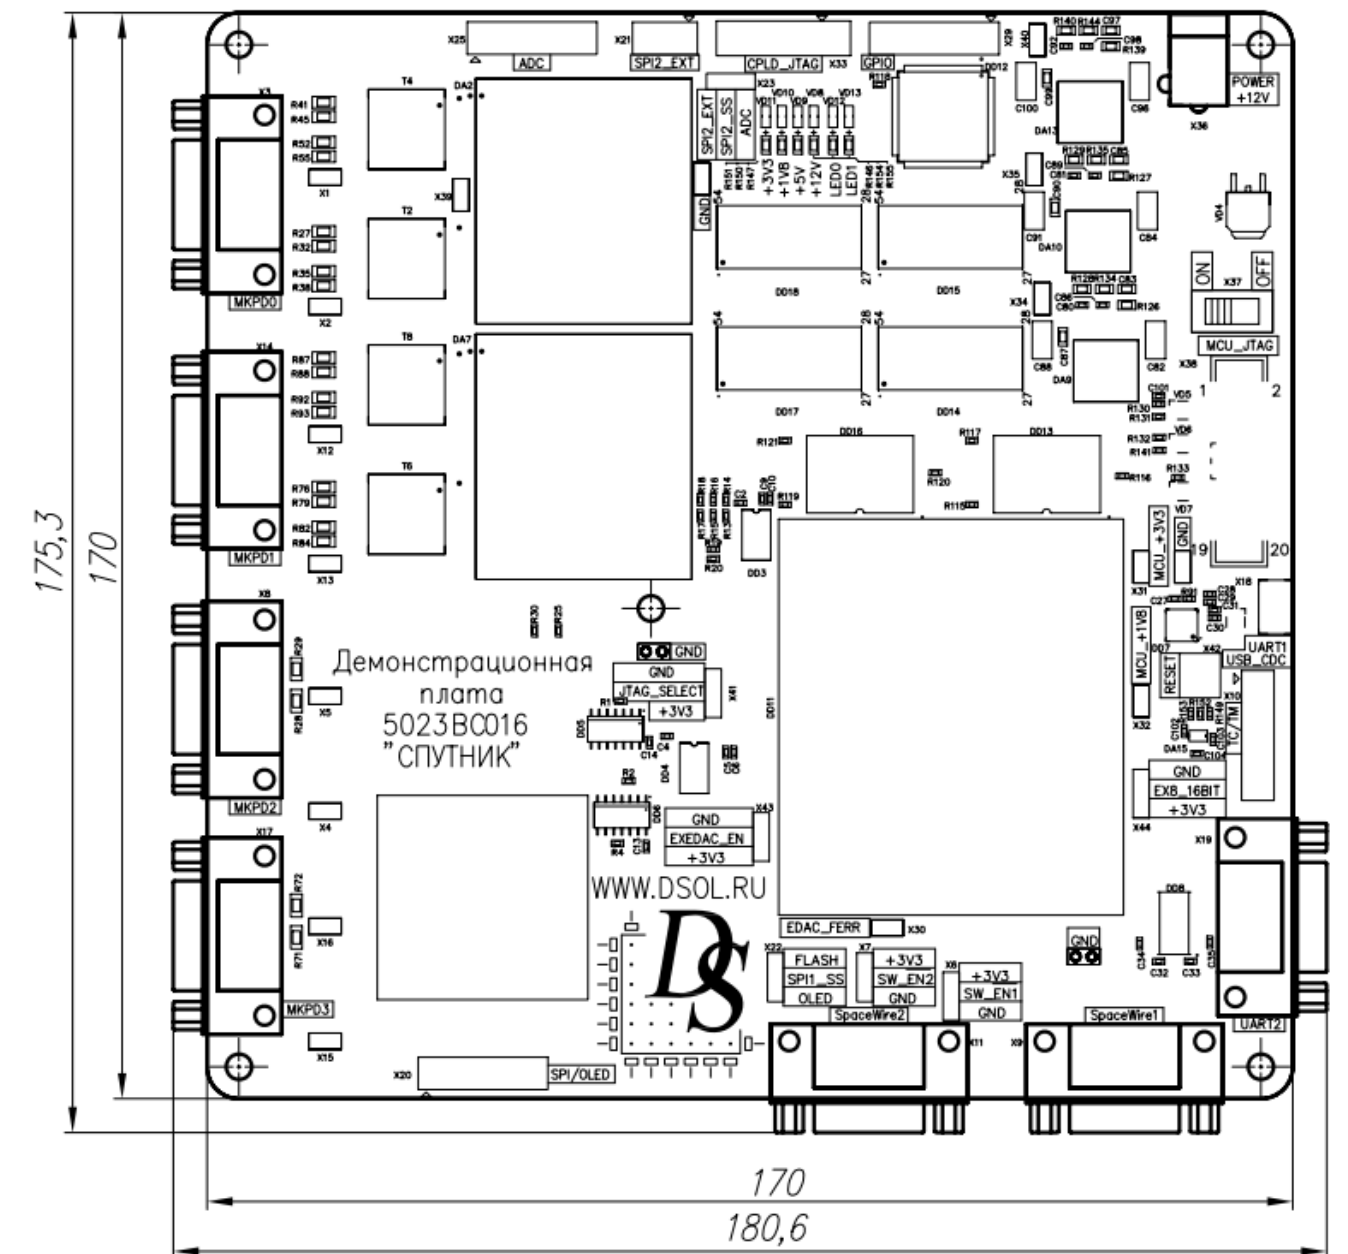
Габаритные и установочные размеры платы «Спутник», вид сверху
